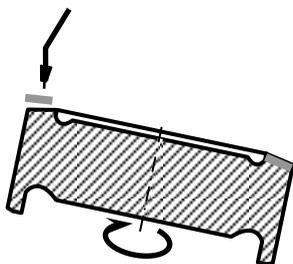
Наплавка аустенитного металла на кромку трубной доски с целью исключения термической обработки подогревателя после сварки замыкающих швов.
